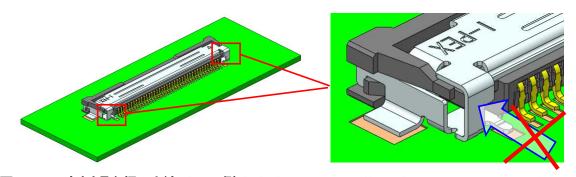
コネクタ取り扱い方法 (NG 例 ) / Fig.4-7 Handling the connector - Bad example
